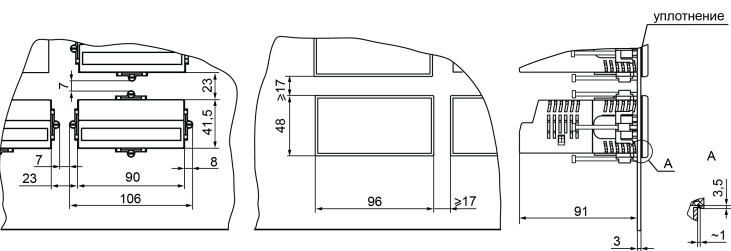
Корпус Щ2 в щите толщиной 3 мм
